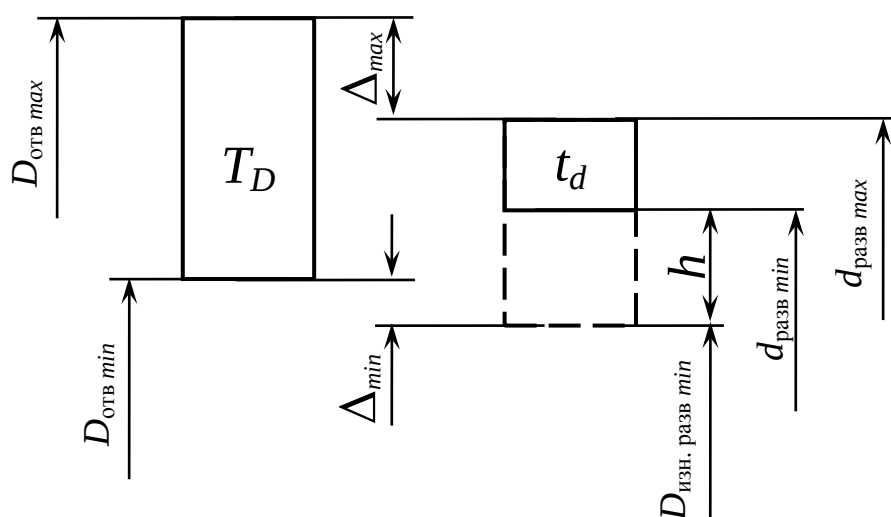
Схема полей допусков разверток: T_D – поле допуска обрабатываемого отверстия, t_d – поле допуска развертки, $D_{изн. разв min}$ – минимальный диаметр изношенной развертки,
